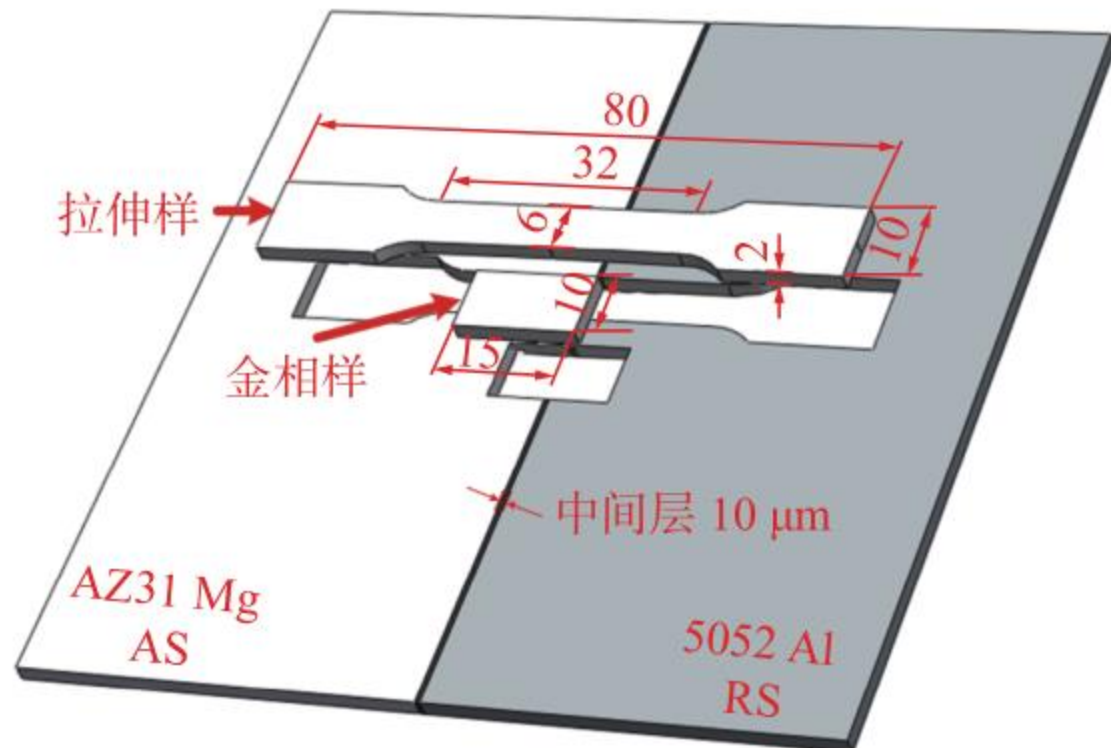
Al/Mg 对接 FSW 装配方式及试样尺寸 (mm)
